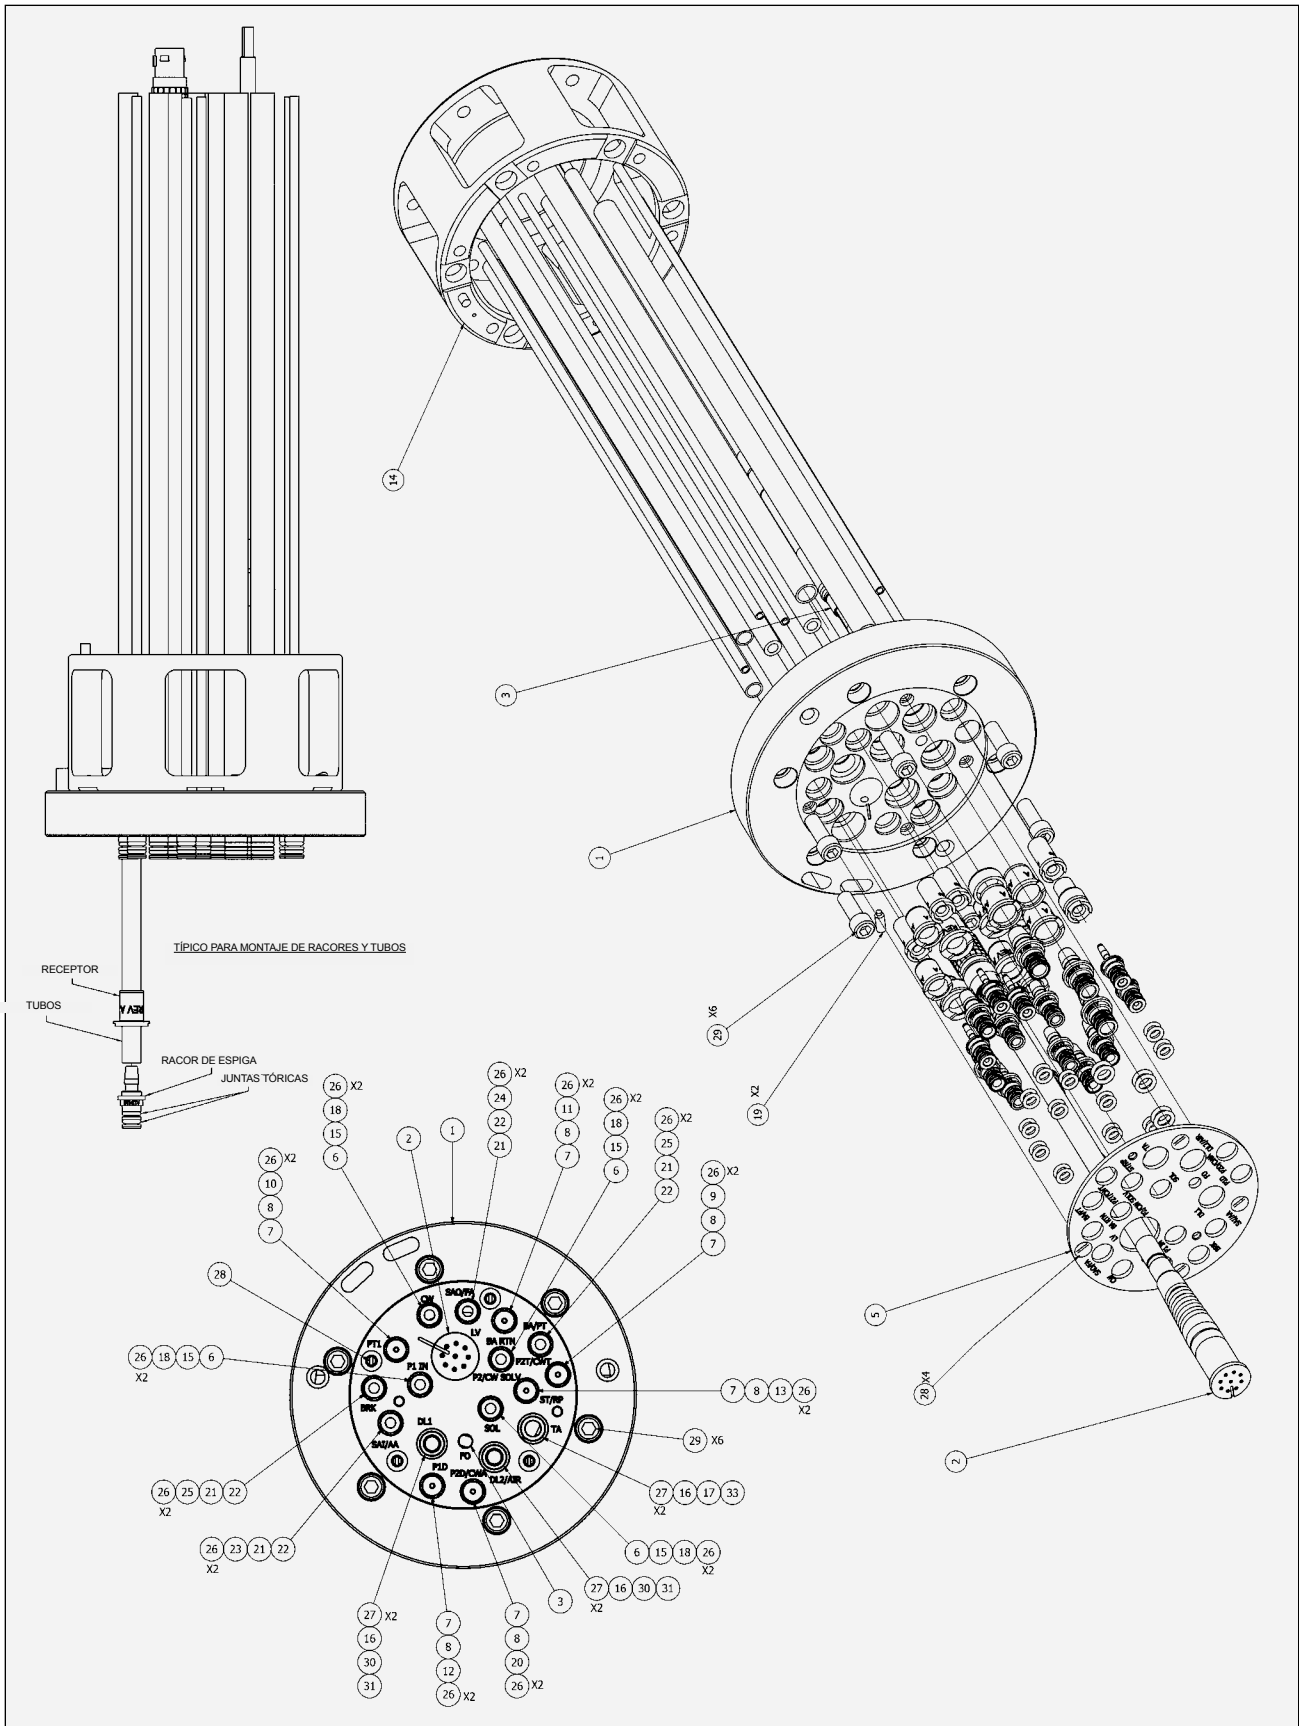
Conjunto del haz de tubos A13436-XXXXXXXXXX
